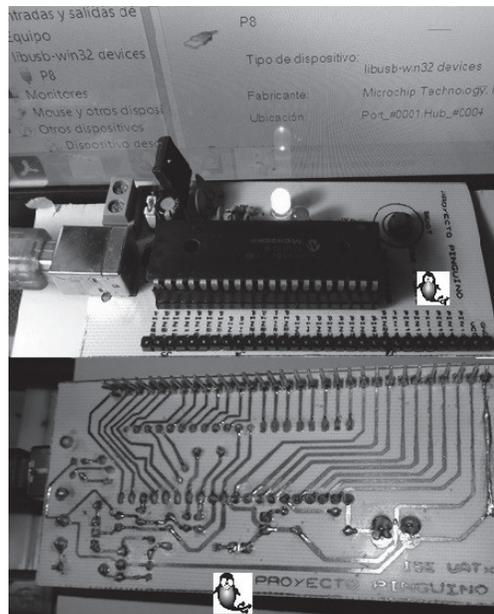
Tarjeta pingüino; vista superior que muestra el driver instalado y la PCB inferior
